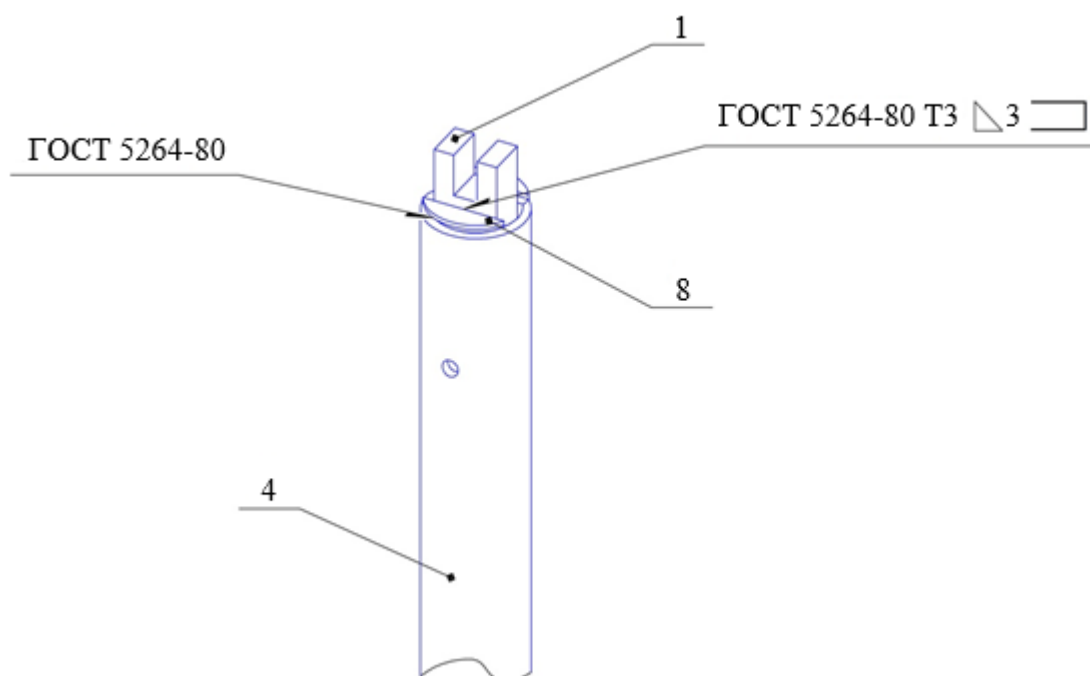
Сборка и сварка штанги позиция. 1 и сегментов позиция. 8
